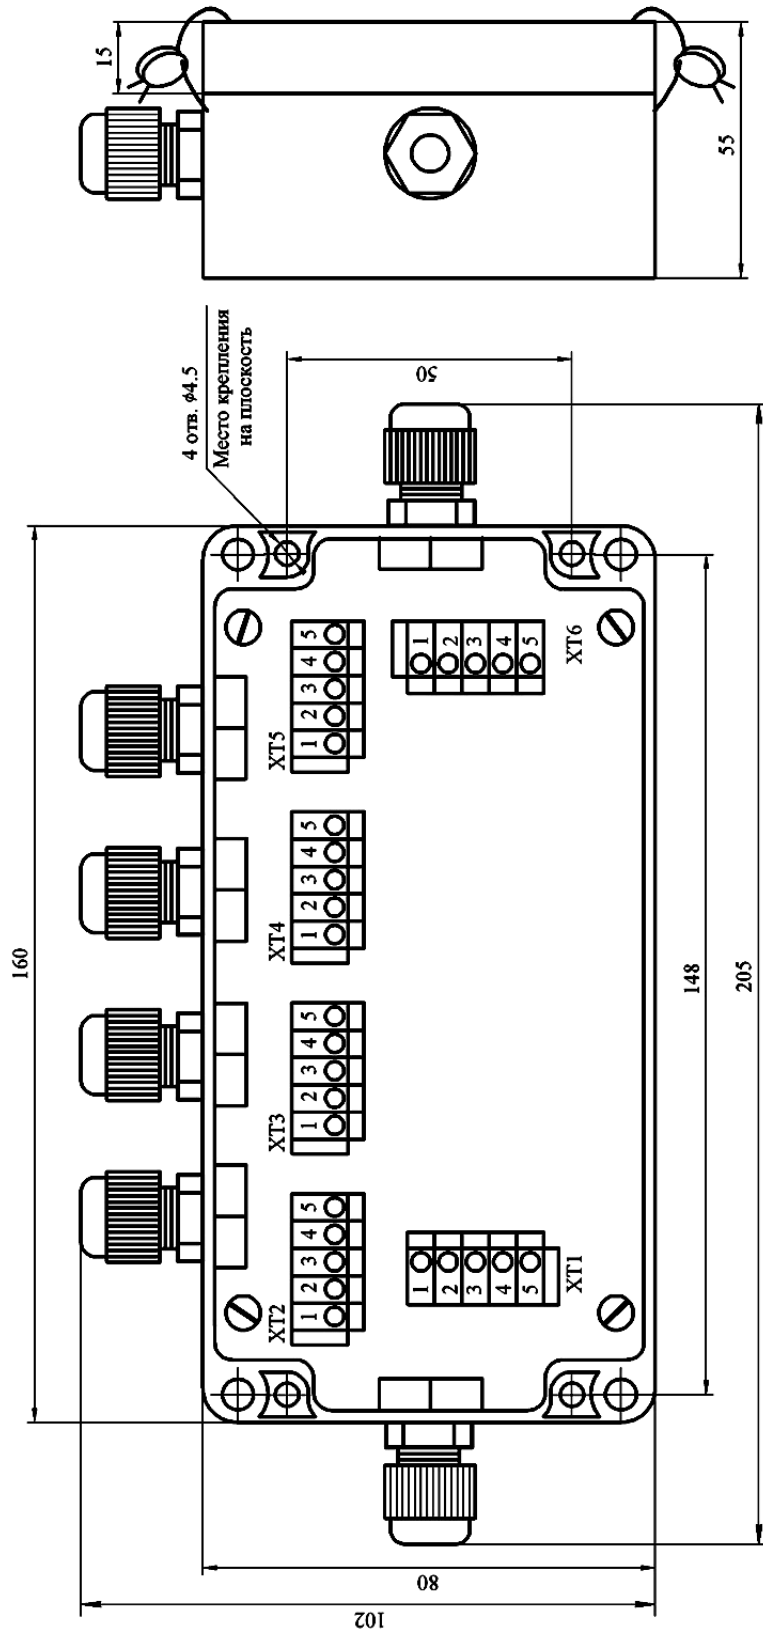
Габаритные и установочные размеры разветвителя SI 4060, ВЭП-04.06
